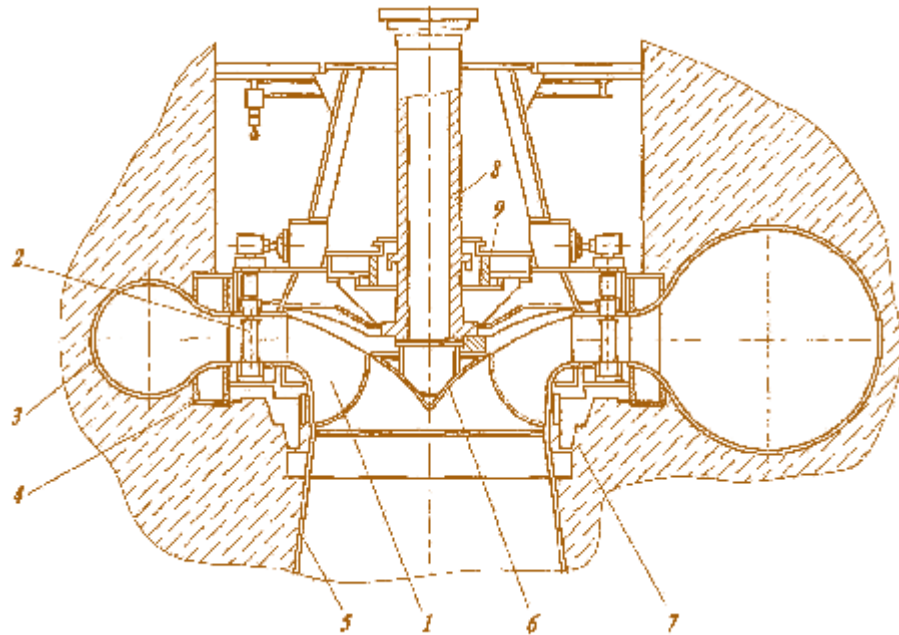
Розріз по насос-турбіні Загорської ГАЕС: 1 – робоче колесо; 2 – лопатки напрямного апарата; 3 – спіральна камера; 4 – статор; 5 – відсмоктувальна труба; 6 – конус робочого колеса; 7 – колектор; 8 – вал; 9 – напрямний підшипник
